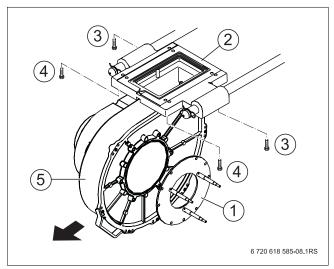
Smontaggio dei componenti del collettore di ventilazione
